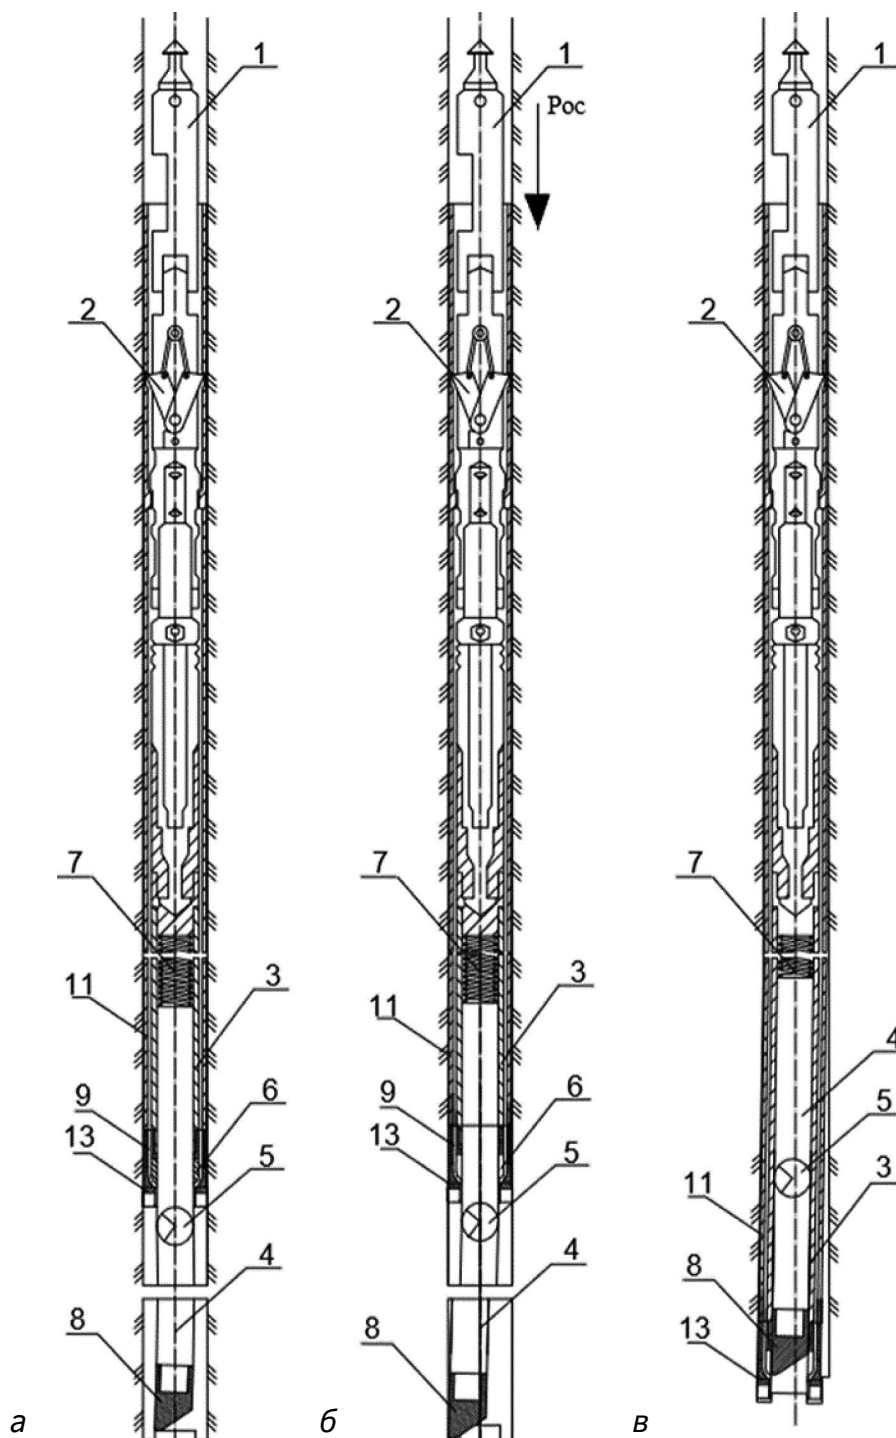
Схема работы съемного отклоняющего комплекса: а — установка отклонителя на забой; б — отклонение штока под действием осевой нагрузки; в — корректировка направления: 1 — ориентатор, 2 — механизм блокирования, 3 — корпус отклоняющего модуля, 4 — направляющий шток, 5 — шарнир, 6 — фиксирующая втулка, 7 — пружина сжатия, 8 — профильный башмак, 9 — промывочные каналы, 11 — металлическая резьба, 13 — алмазная коронка
